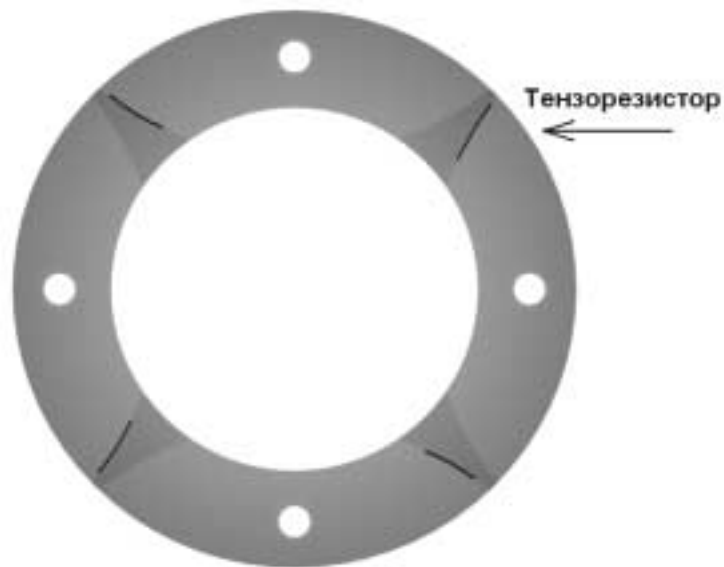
Схема установки тензорезисторов на прорези корпуса правой полумуфты станка 16K20Φ3
